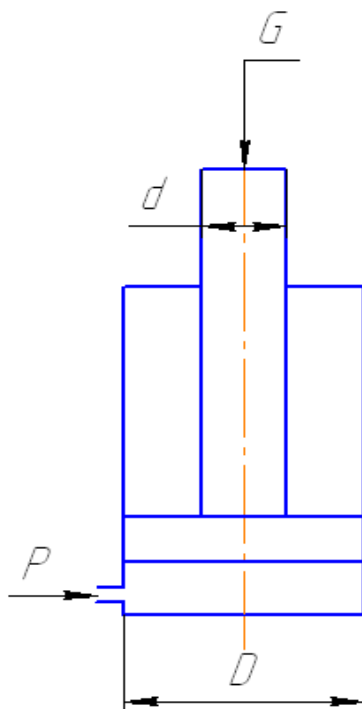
Розрахункова схема робочого гідроциліндра
